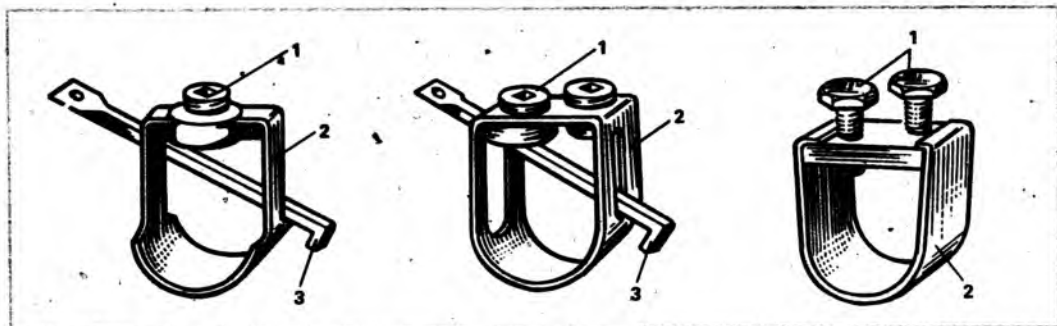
Конструкции косных колец с винтами: 1 — винт; 2 — кольцо; 3 — ключ
